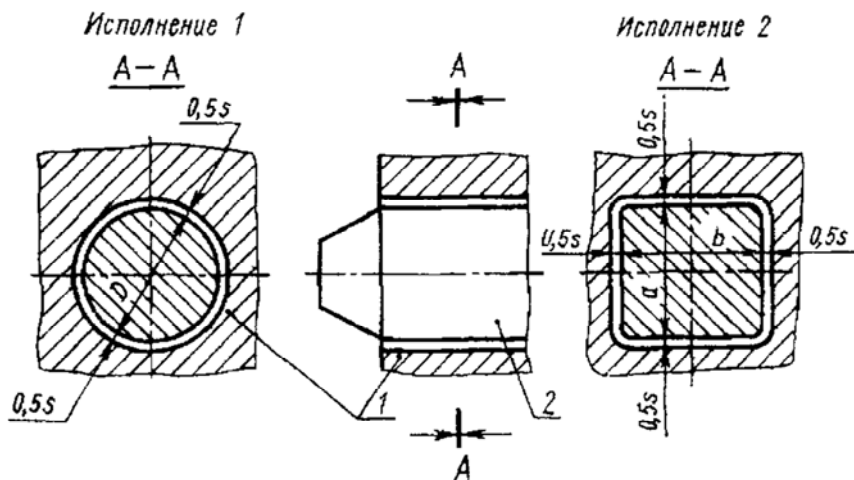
Примеры расположения зазоров между направляющими металлическими стержней и металлической формой:
